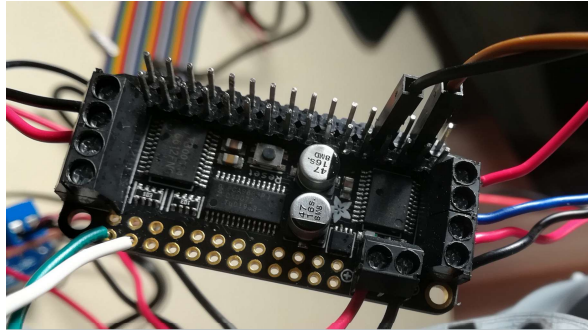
Montaje de Motor Stepper FeatherWing de Adafruit
